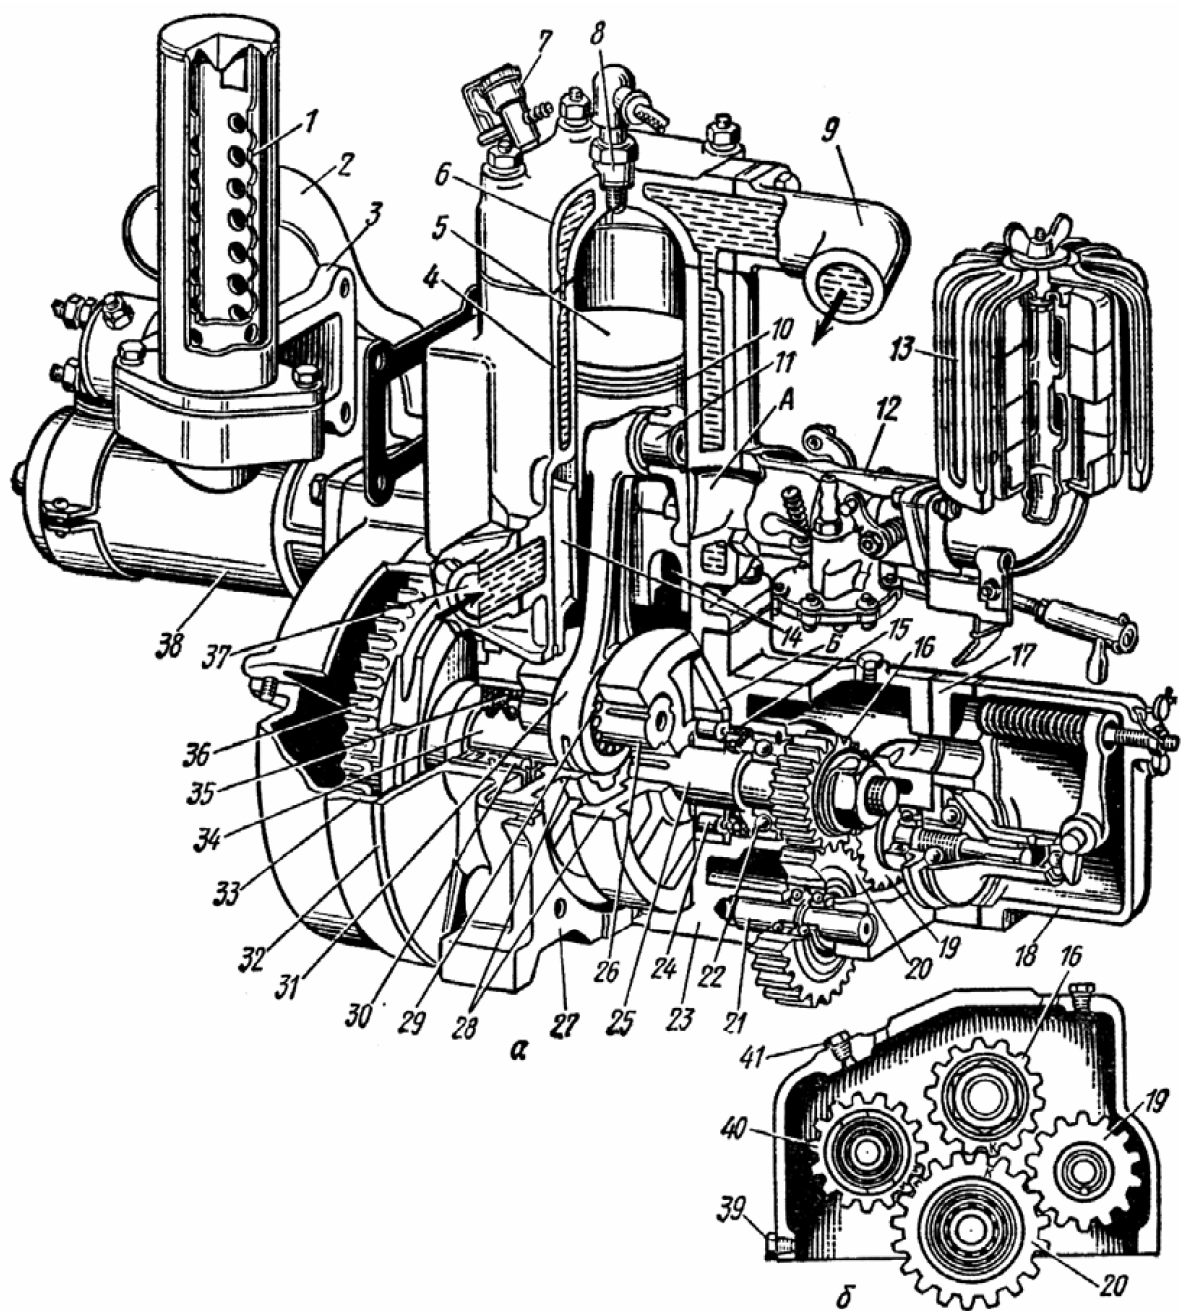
Пусковой двигатель П-10УД (а) и схема расположения шестерен (б):
